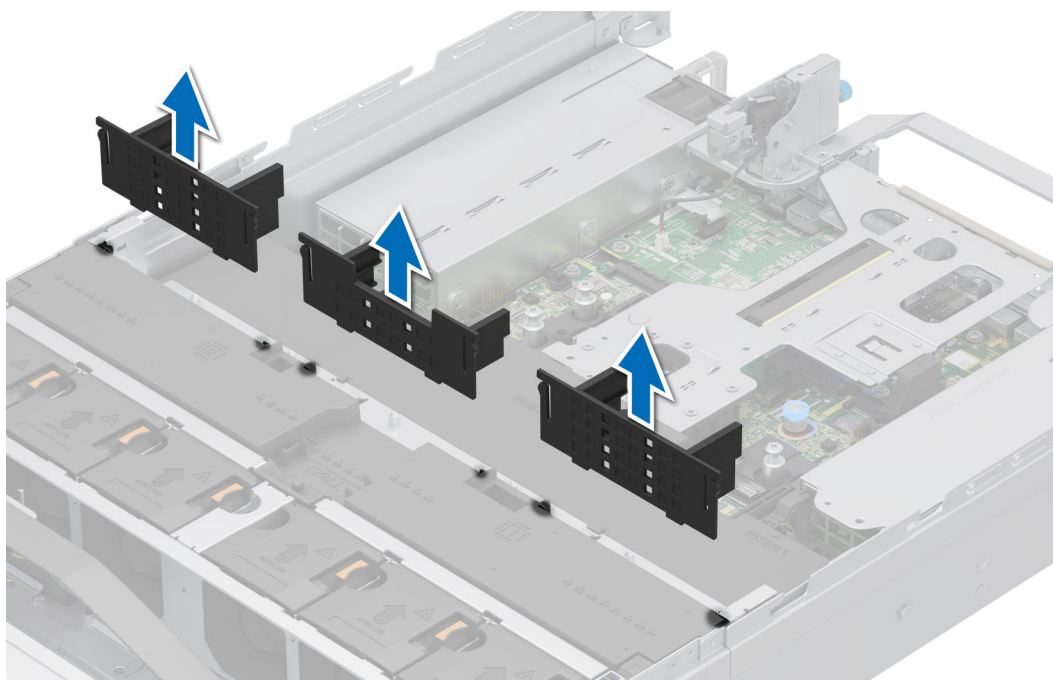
Entfernen des GPU-Kühlgehäuses
